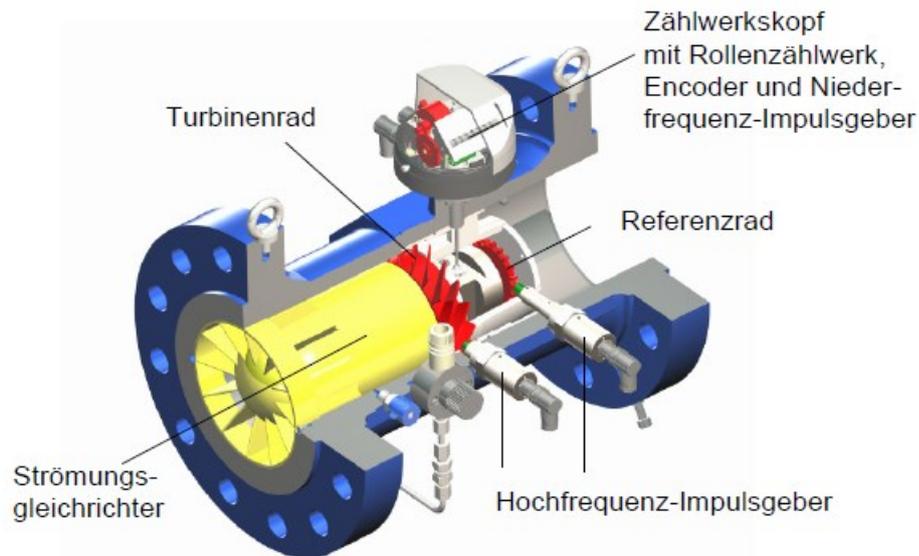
Schnittzeichnung Turbinenradgaszähler
